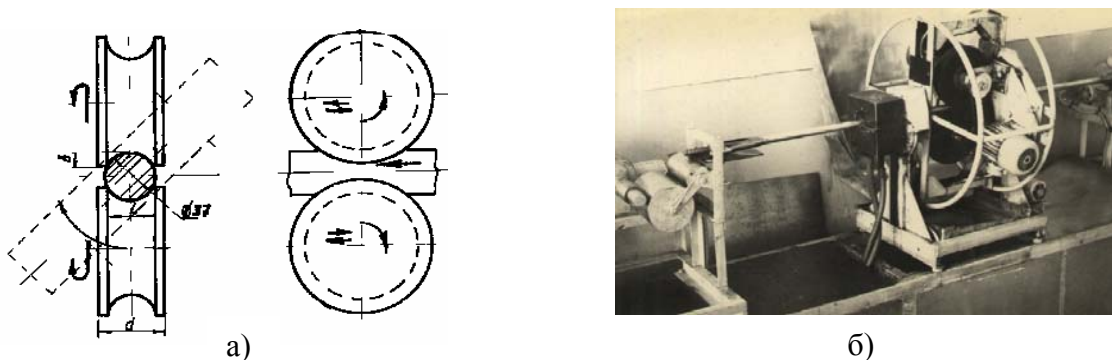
Схема рабочей головки (а) и установка для абразивной обработки (б) трубчатых элементов из лент [4].
